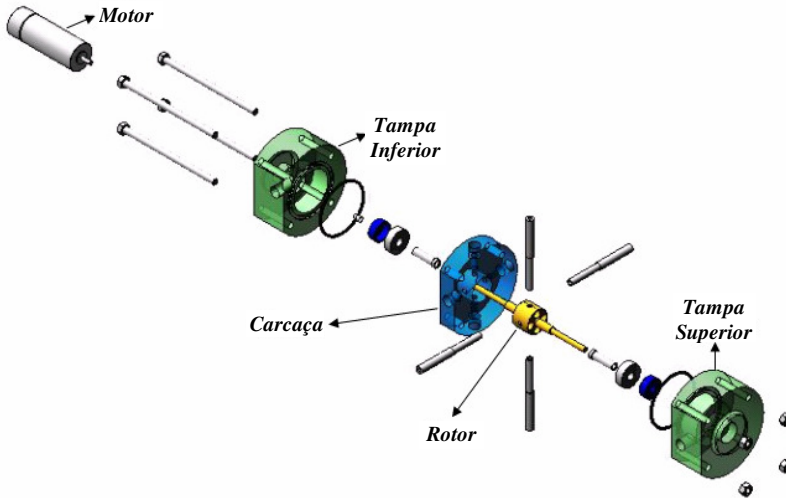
Componentes do protótipo da Válvula Rotativa Inercial em vista explodida.
